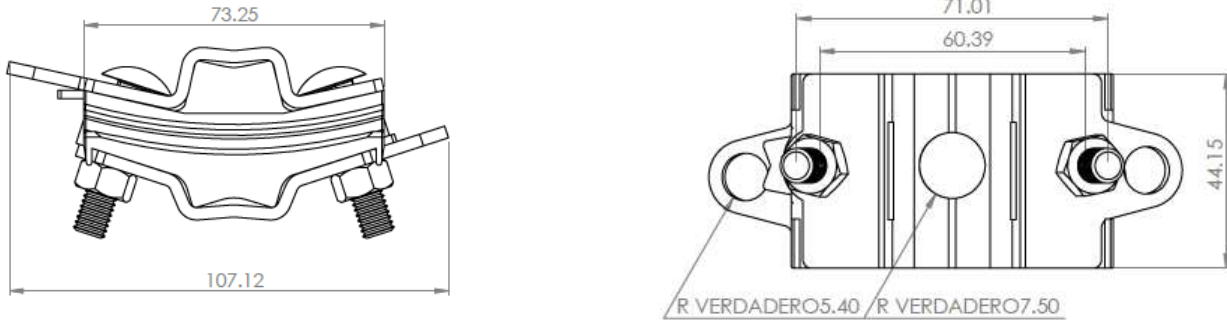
Vistas y dimensiones de componentes del código HTS-1F-F8FRP
